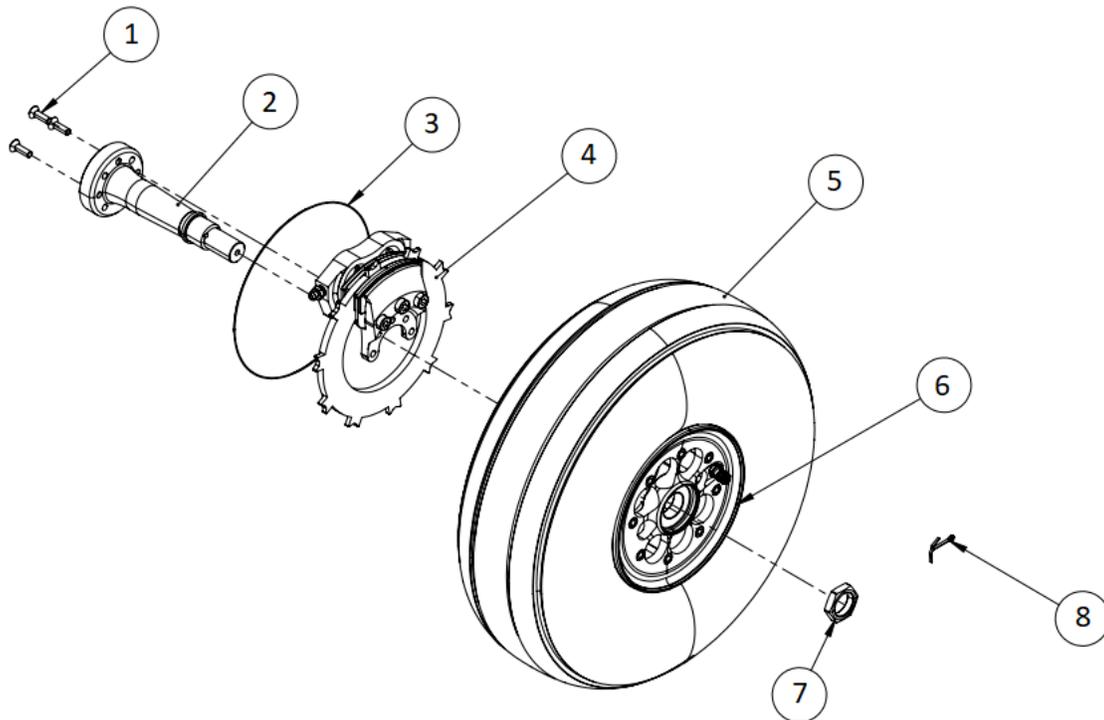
Conjunto do trem de pouso principal.
